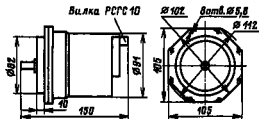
22 Габаритные и установочные размеры двигателя АГ/4 150-6К
